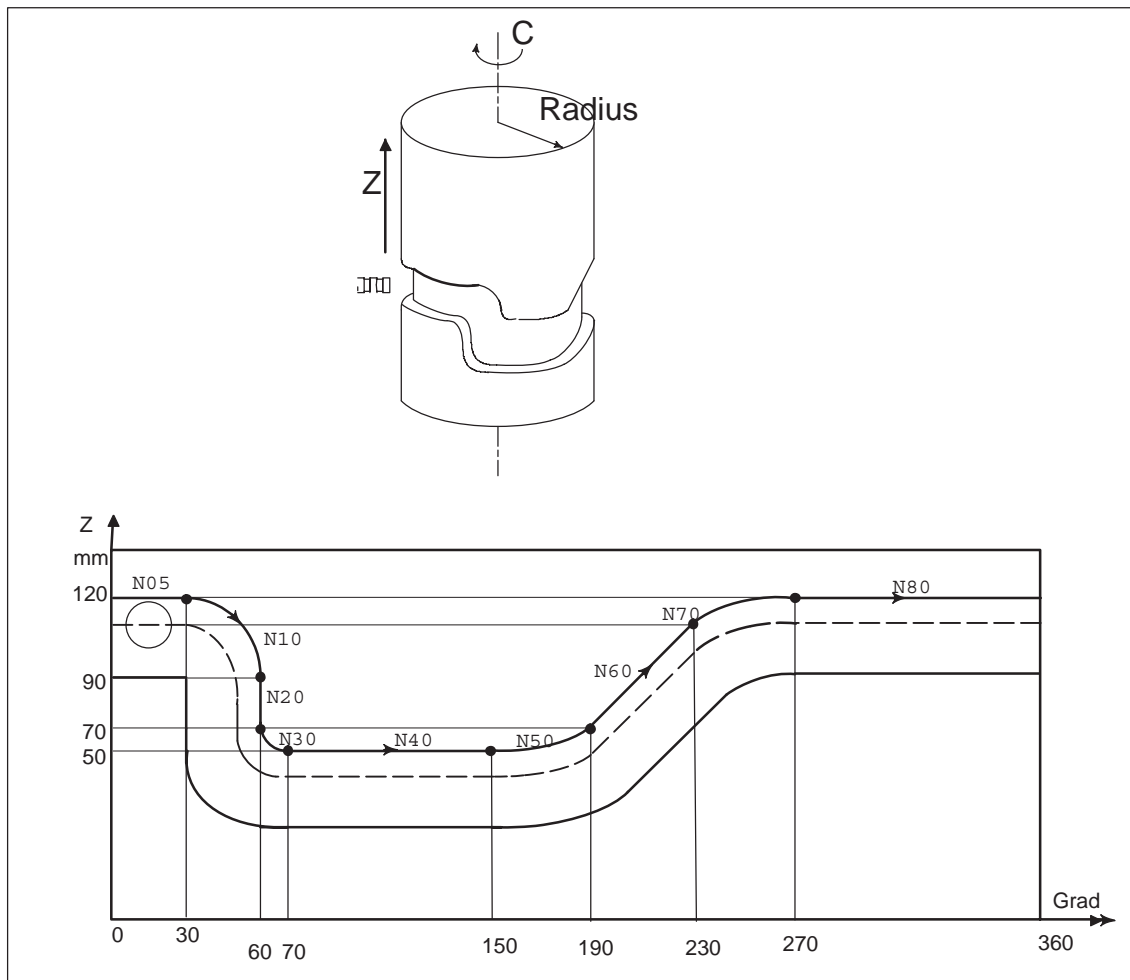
Beispiel für die Zylinderinterpolation G07.1
